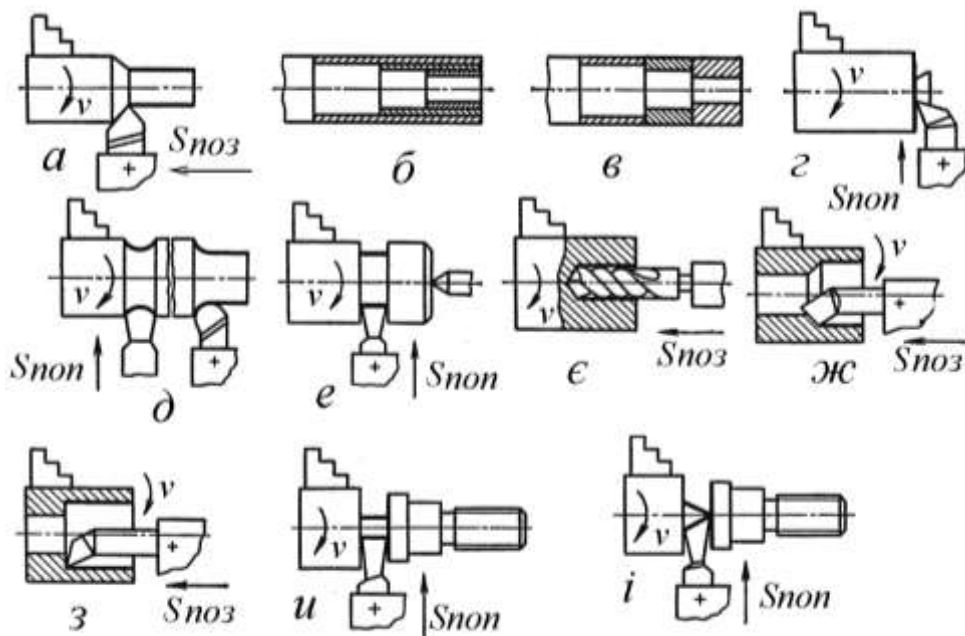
Схеми обробки заготовок на токарних верстатах
